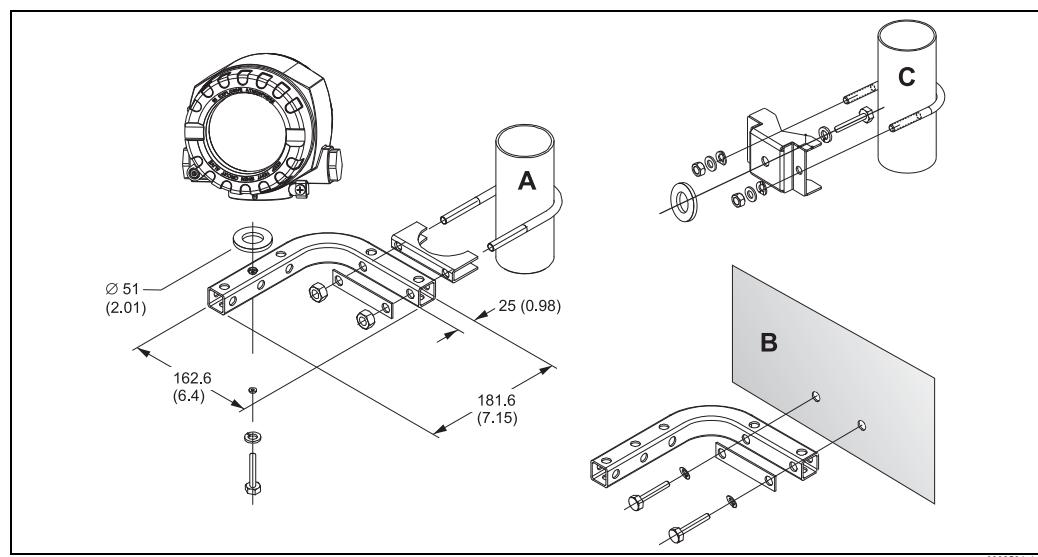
Montage des Feldtransmitters mit Montagehalter, siehe Kap. 'Zubehör'. Abmessungen in mm (in)
